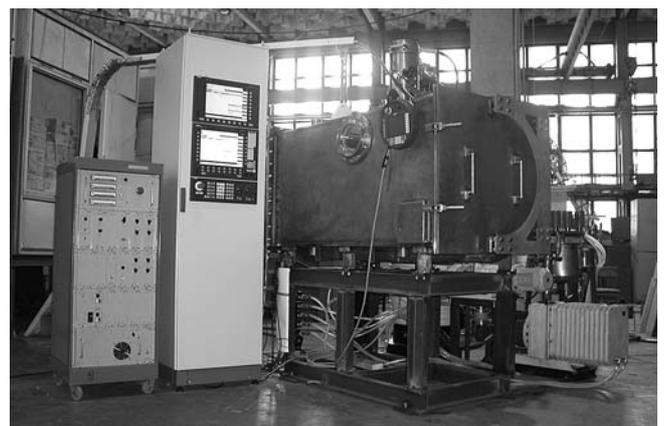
Установка электронно-лучевой сварки ЭЛУ-08КП
